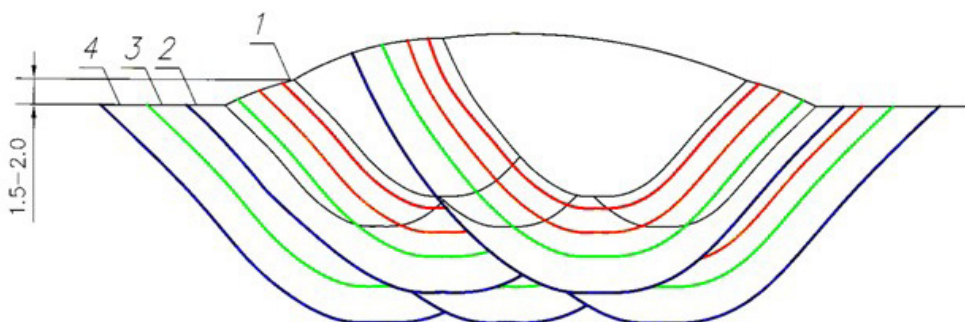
Крупнозернистая структура в сварном соединении
